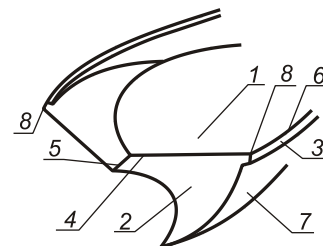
Поверхности и лезвия рабочей части винтового сверла
